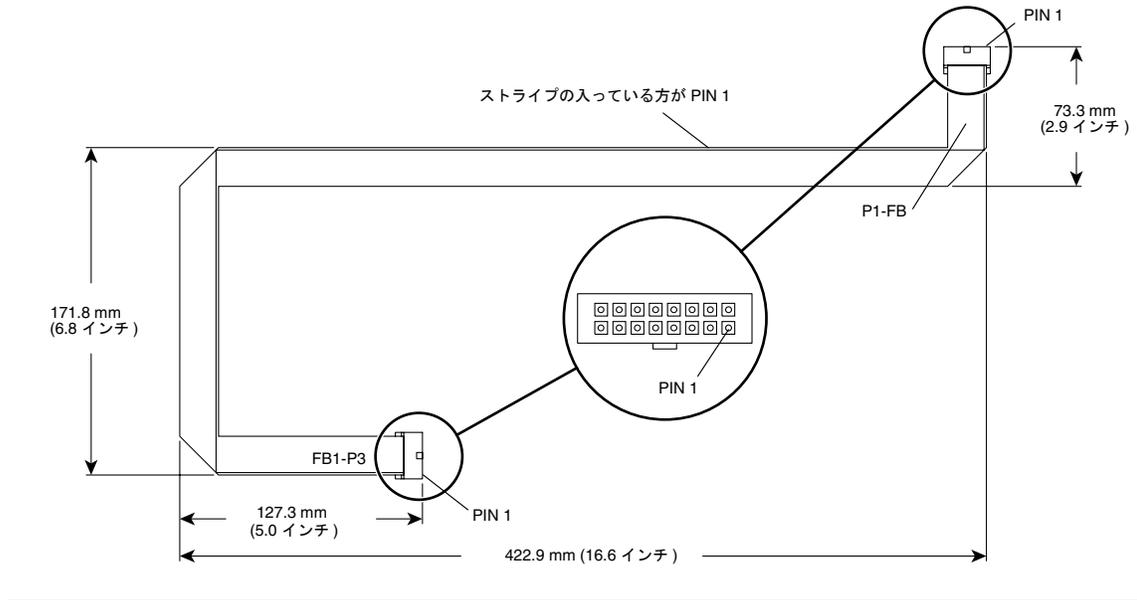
Fan I²C Cable、Rear Lower (パーツ番号 530-2770)
